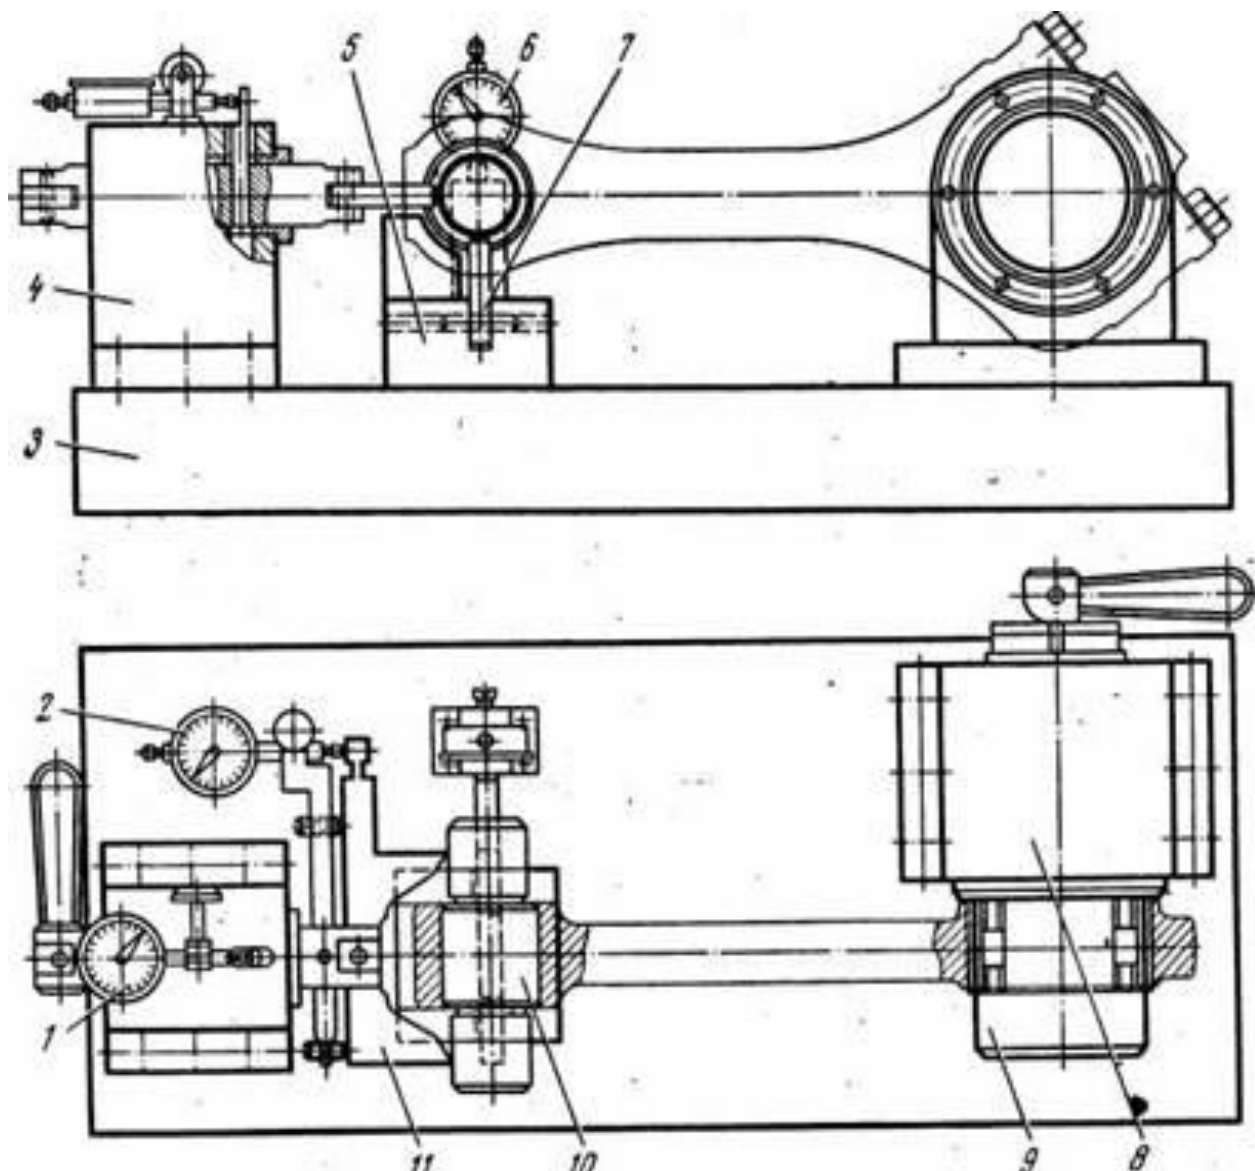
Приспособление для контроля шатуна: 2, 6 — индикатор; 3 — основание; 4 — корпус; 5 — стойка; 7 — упор; 9 — базовый палец; 10 — установочный палец; U — скоба
